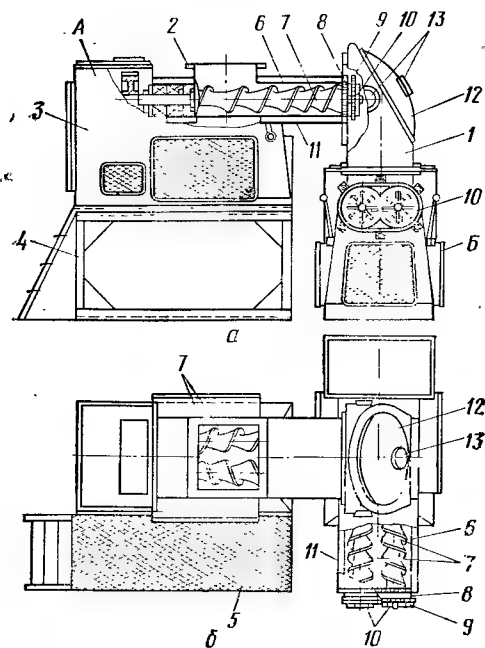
Двухступенчатый двухвинтовой шнек-пресс:
